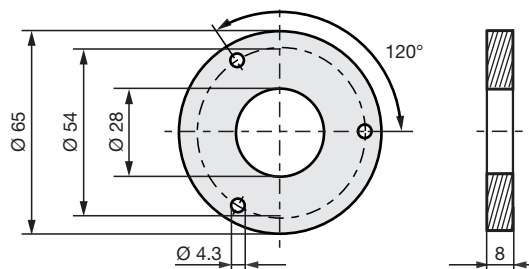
Accessori speciali BTL-P-1028-15R
